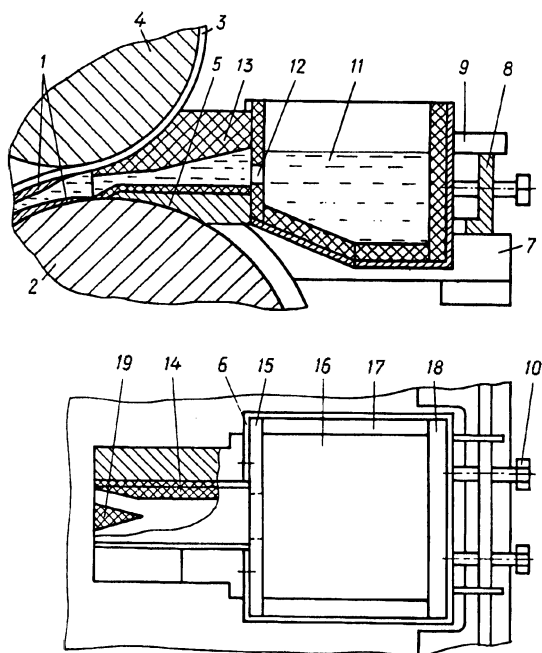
Конструкция распределителя расплава: 1 — отливка; 2 — колесо; 3 — лента; 4 — прижимной валок; 5 — корпус лотка; 6 — кожух; 7 — рама; 8 — угольник; 9 — планка; 10 — винт; 11 — расплав; 12 — паз питателя; 13 — вставка; 14 — 18 — теплоизоляция
